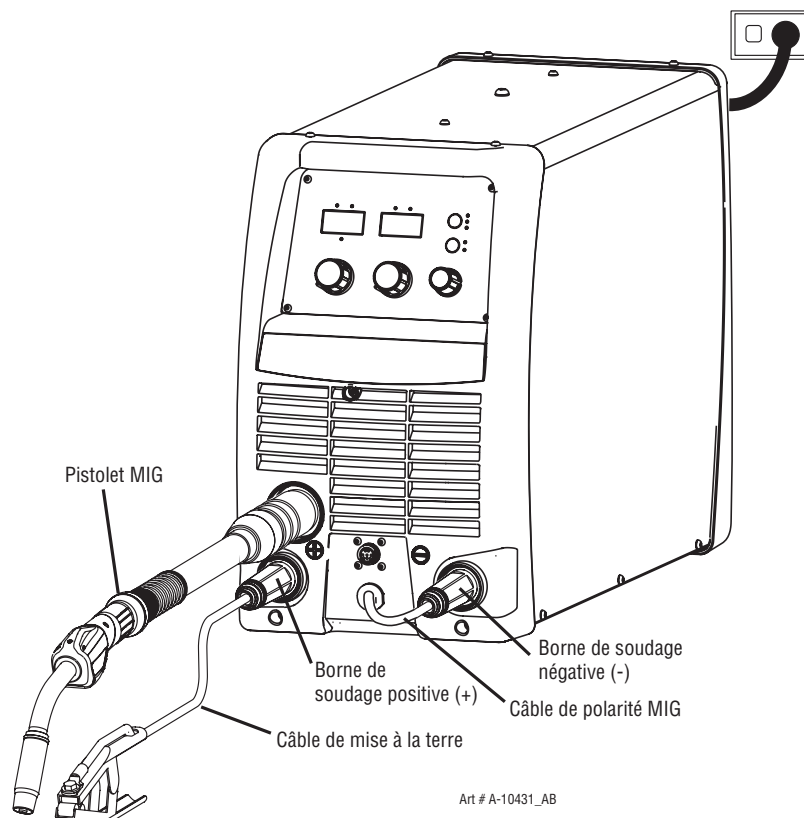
Configuration pour le soudage MIG avec le fil MIG sans gaz
